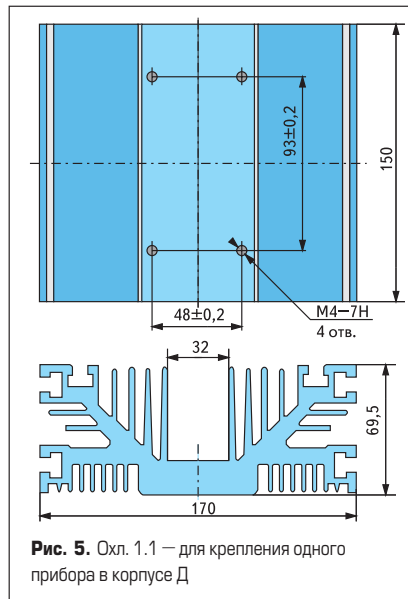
Охл. 1.1 — для крепления одного прибора в корпусе D
